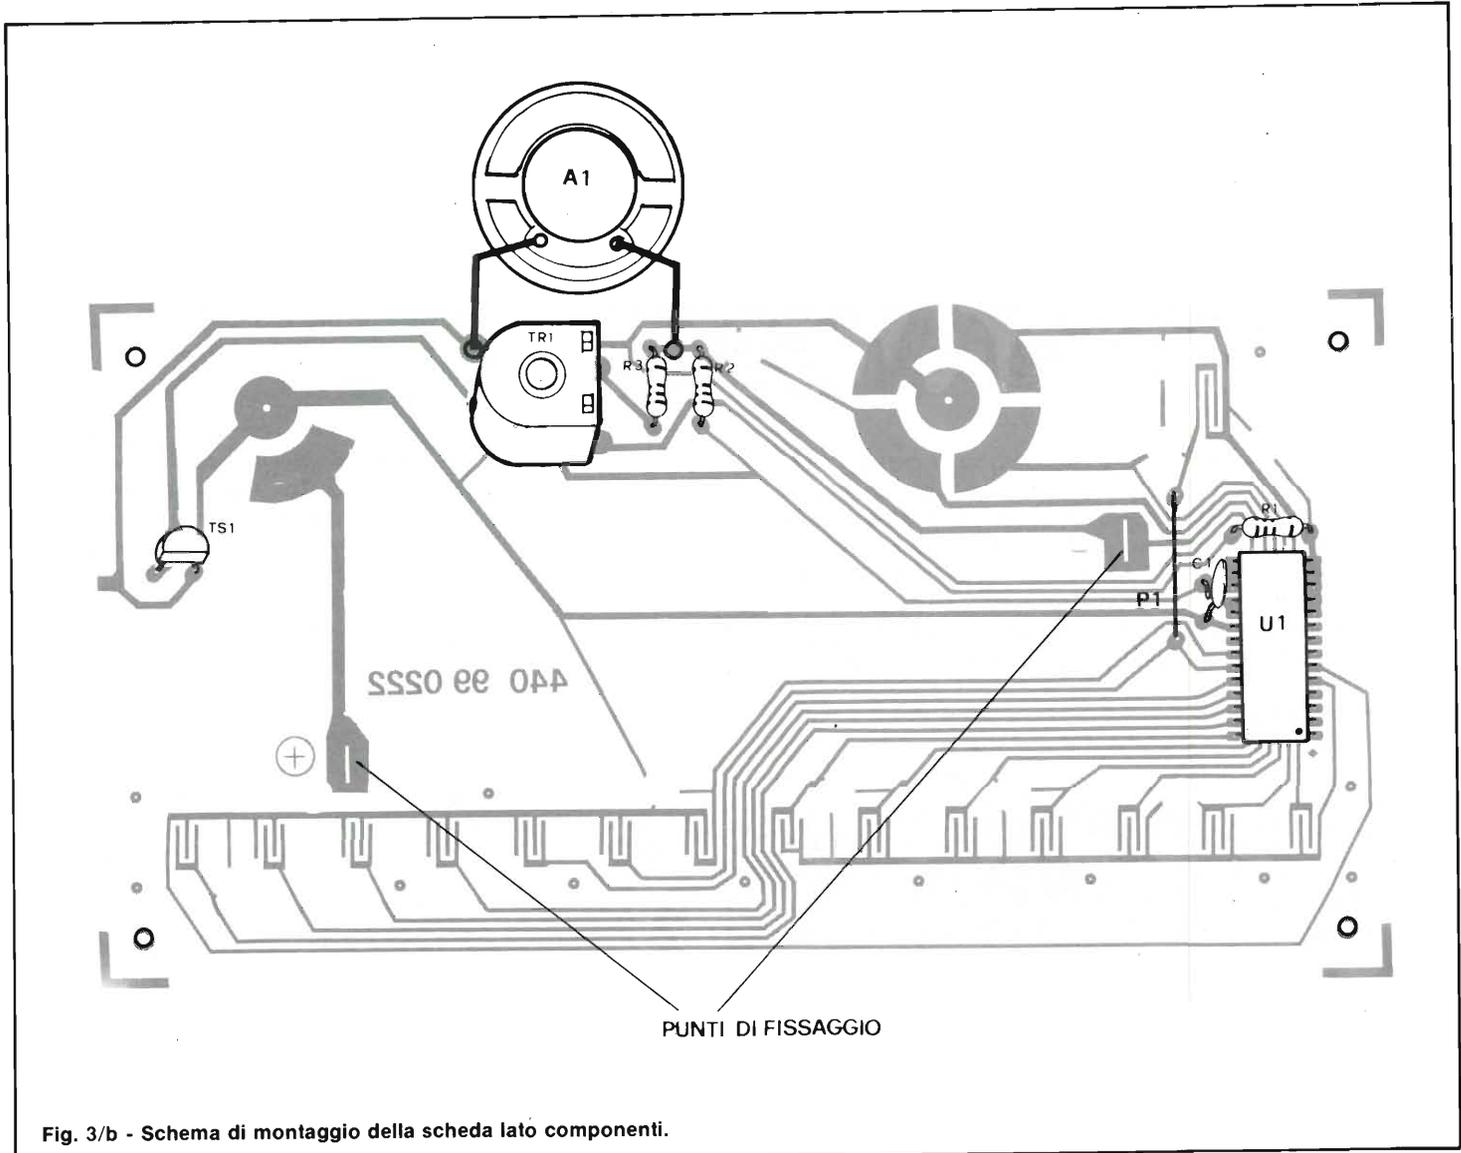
/b - Schema di montaggio della scheda lato componenti.
